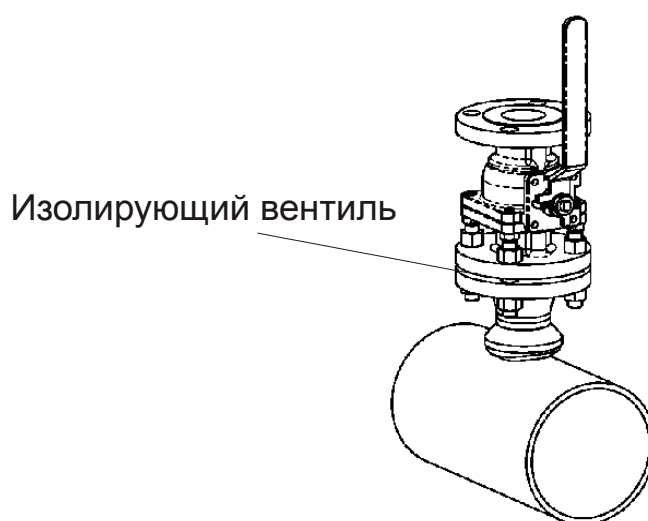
Установка и ориентация изолирующего вентиля на фланец монтажного узла
